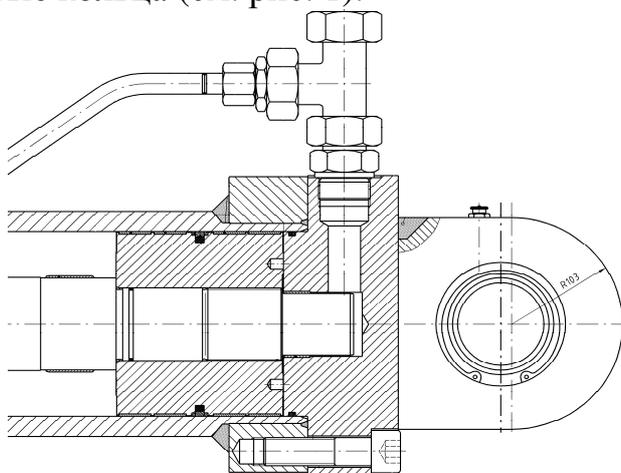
Уплотнение поршня металлическими поршневыми кольцами
